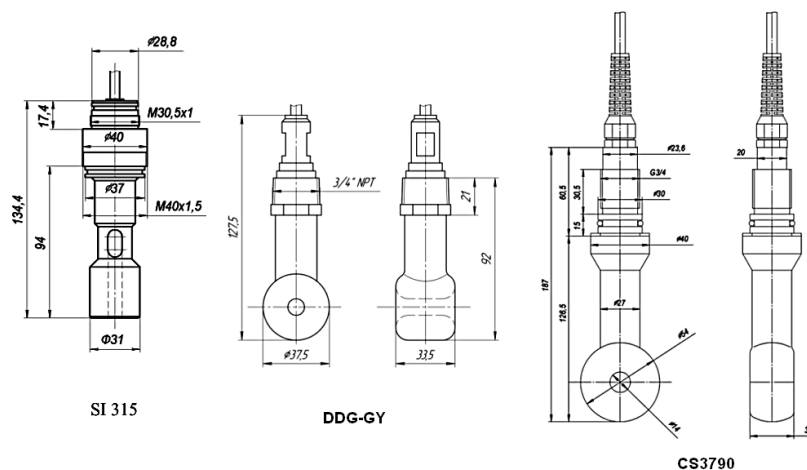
Габаритные и монтажные размеры индуктивных датчиков
